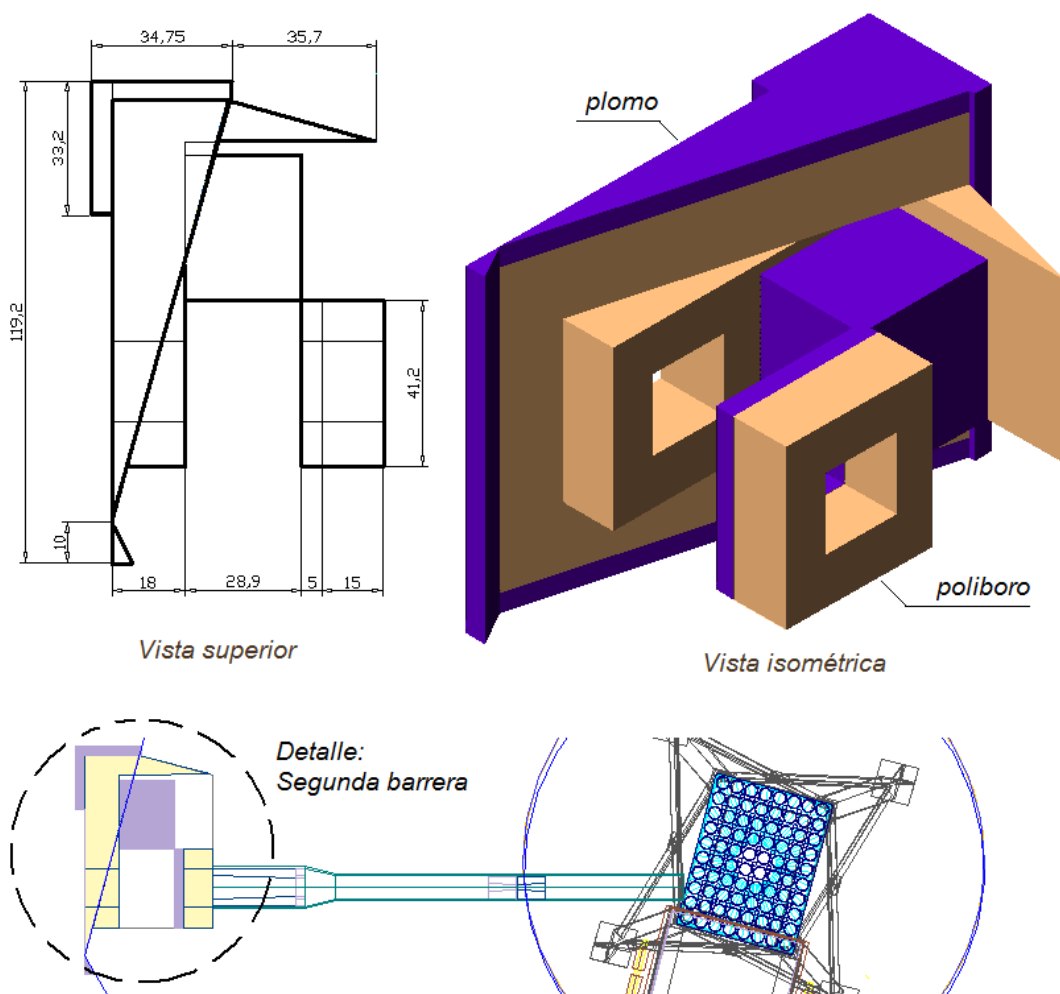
Diseño de segunda barrera (unidades en cm).
